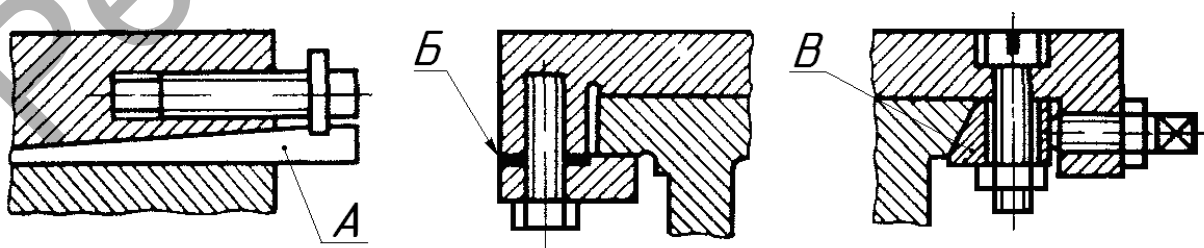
Регулировка зазоров в направляющих скольжения
